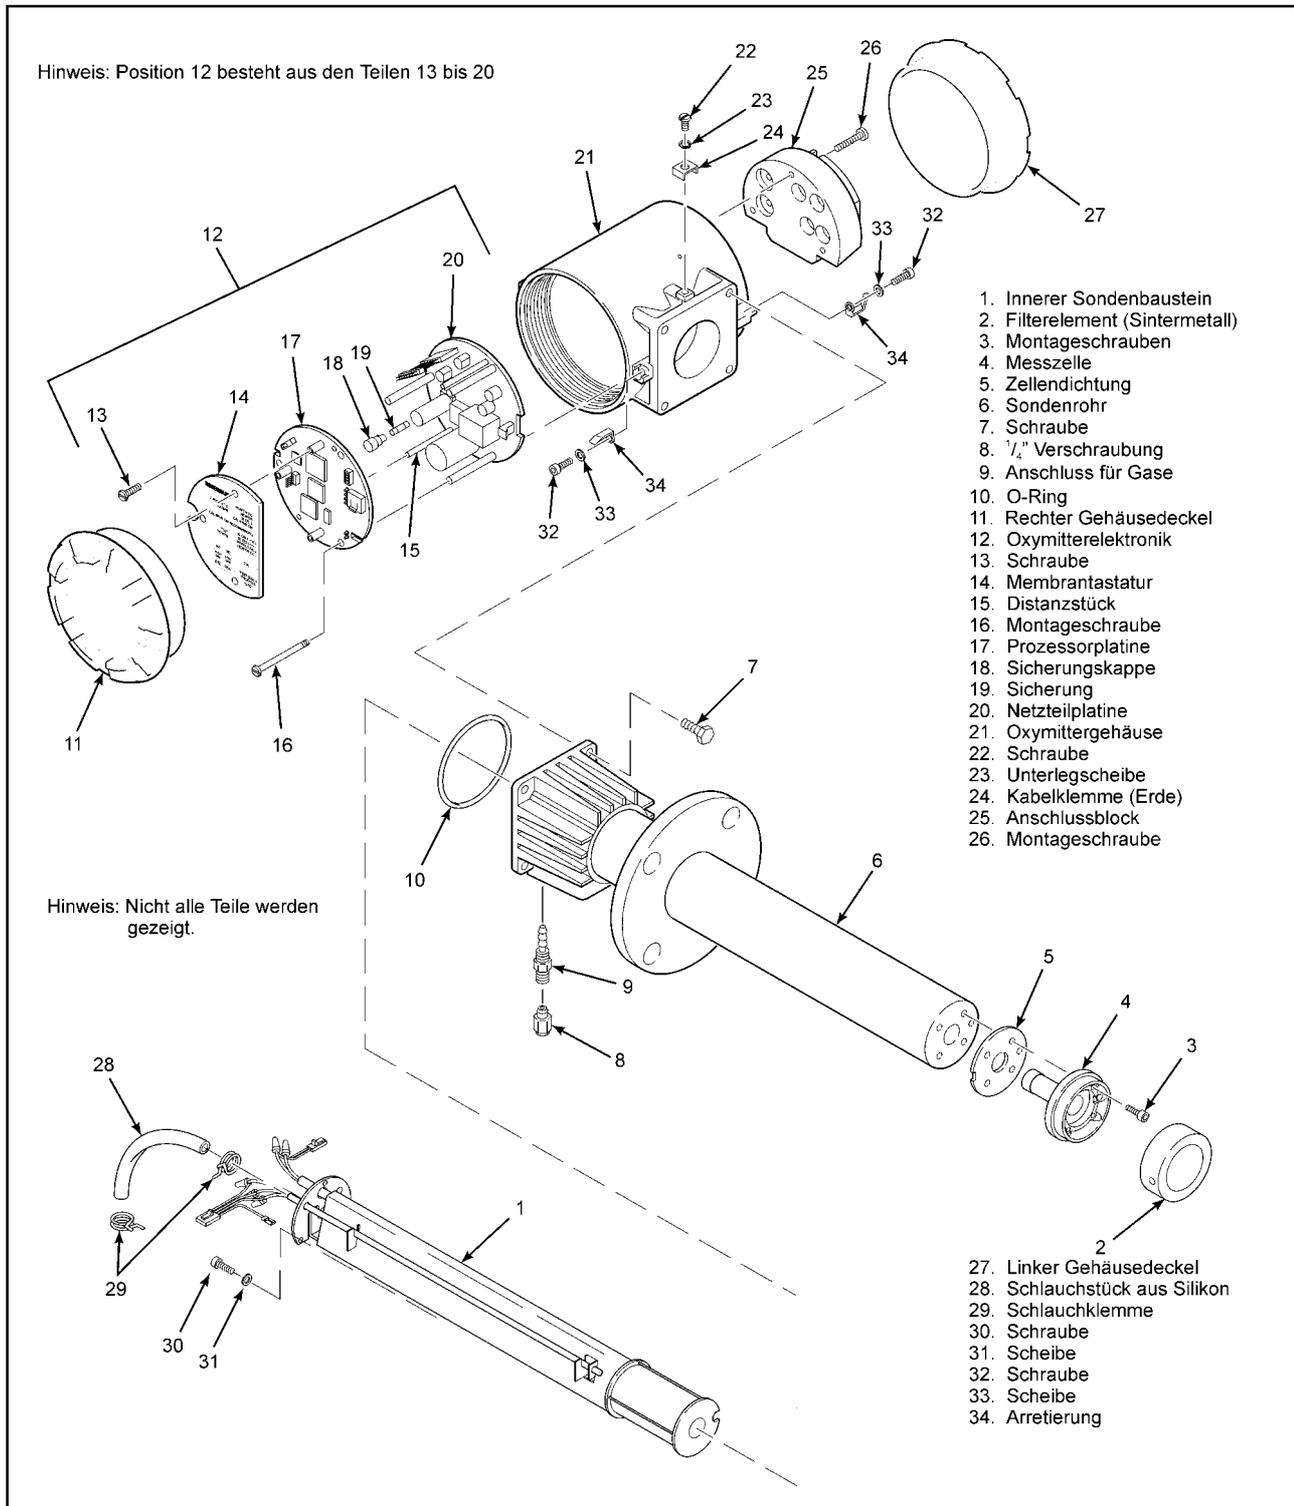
Explosionszeichnung OXYMITTER 4000
